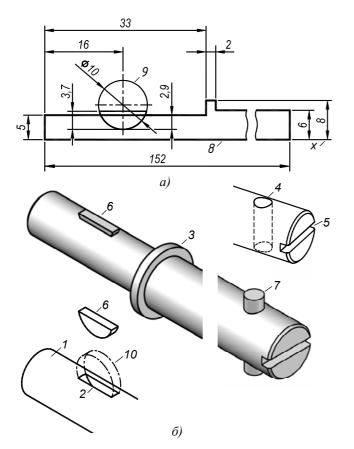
Вал в сборе: a – контуры; δ – элементы вала в сборе;
